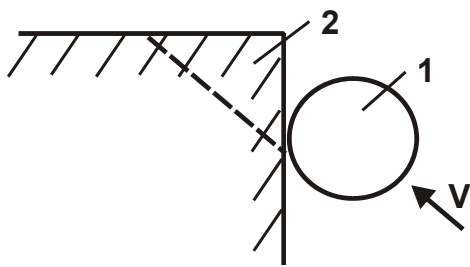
Схема взаємодії абразивного зерна (1) із кромкою заготовки (2)
